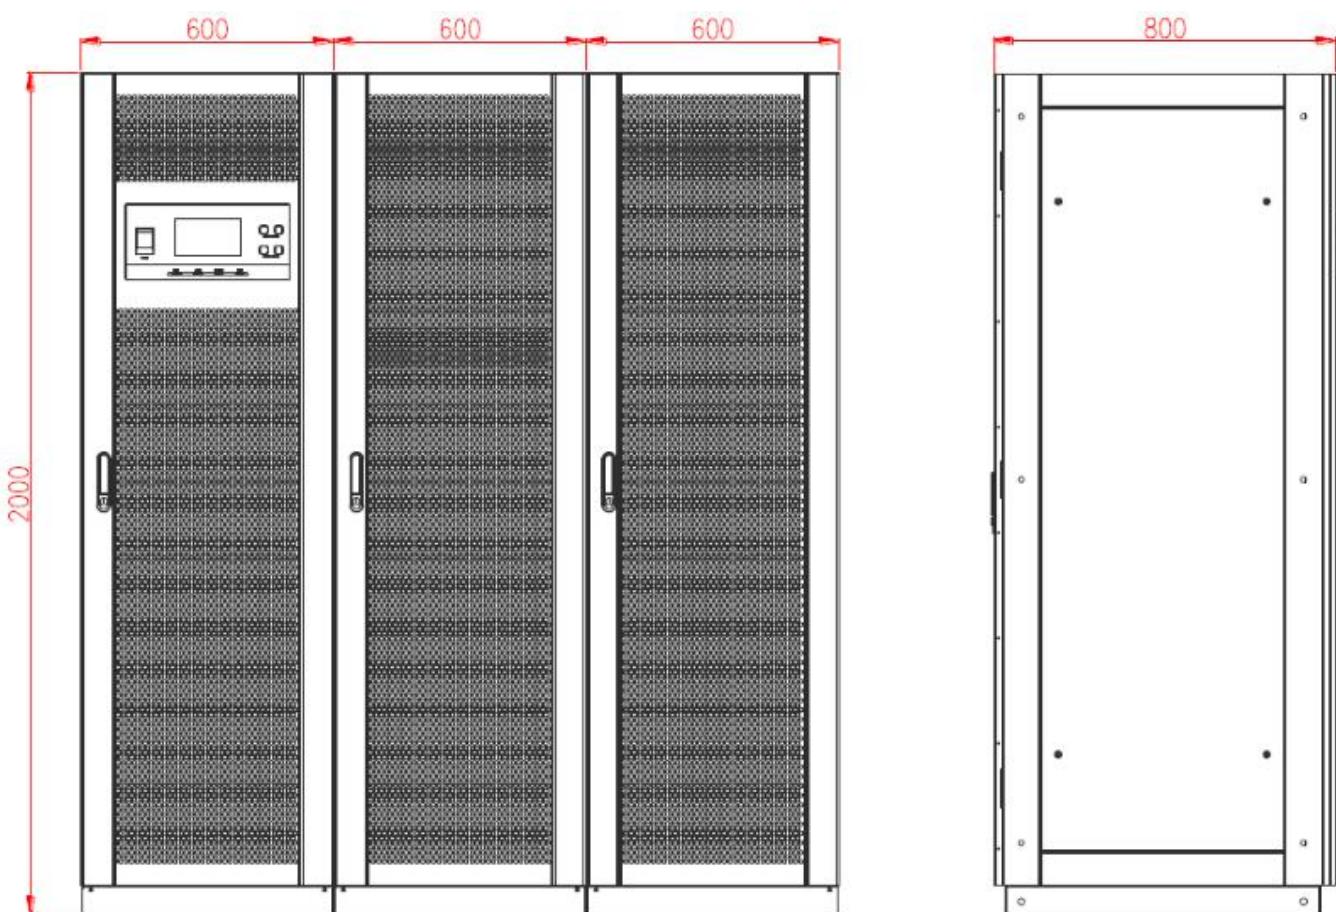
Внешний вид и габаритные размеры корпуса ИБП Monolith XM120, XM200
